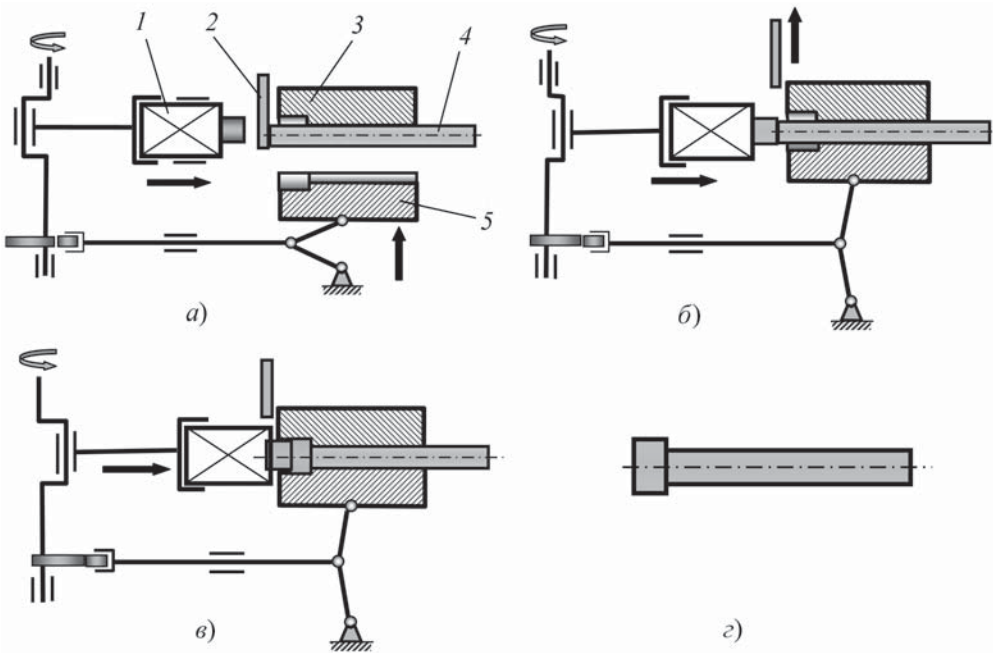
Кинематическая схема ГКМ и этапы штамповки прутковой заготовки:
